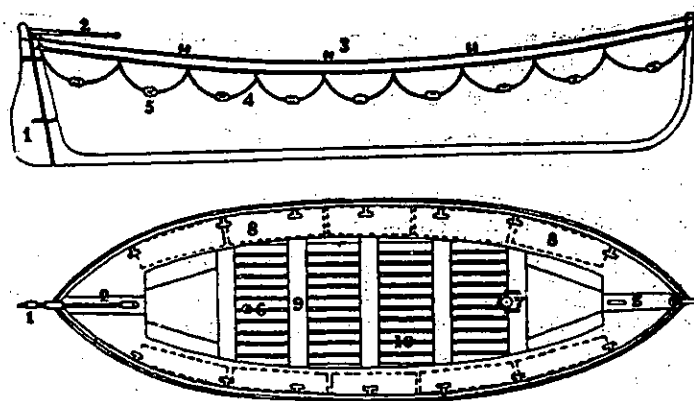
Perfil longitudinal y sección en planta de un típico bote salvavidas de buque mercante:
